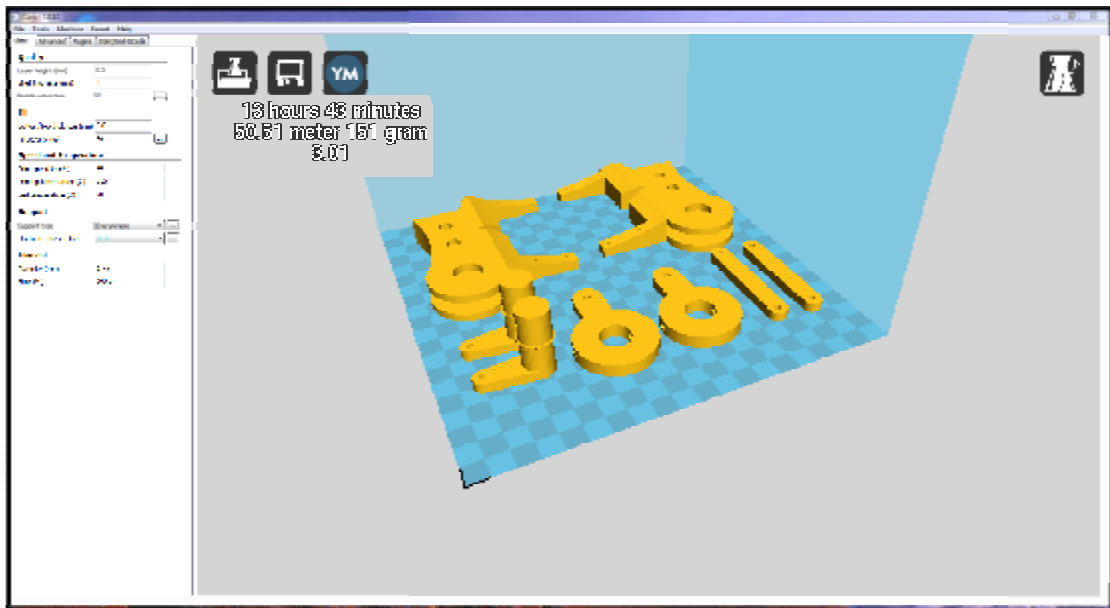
Already Assembly Άρθρωσης Γονάτου (Knee Joint).
